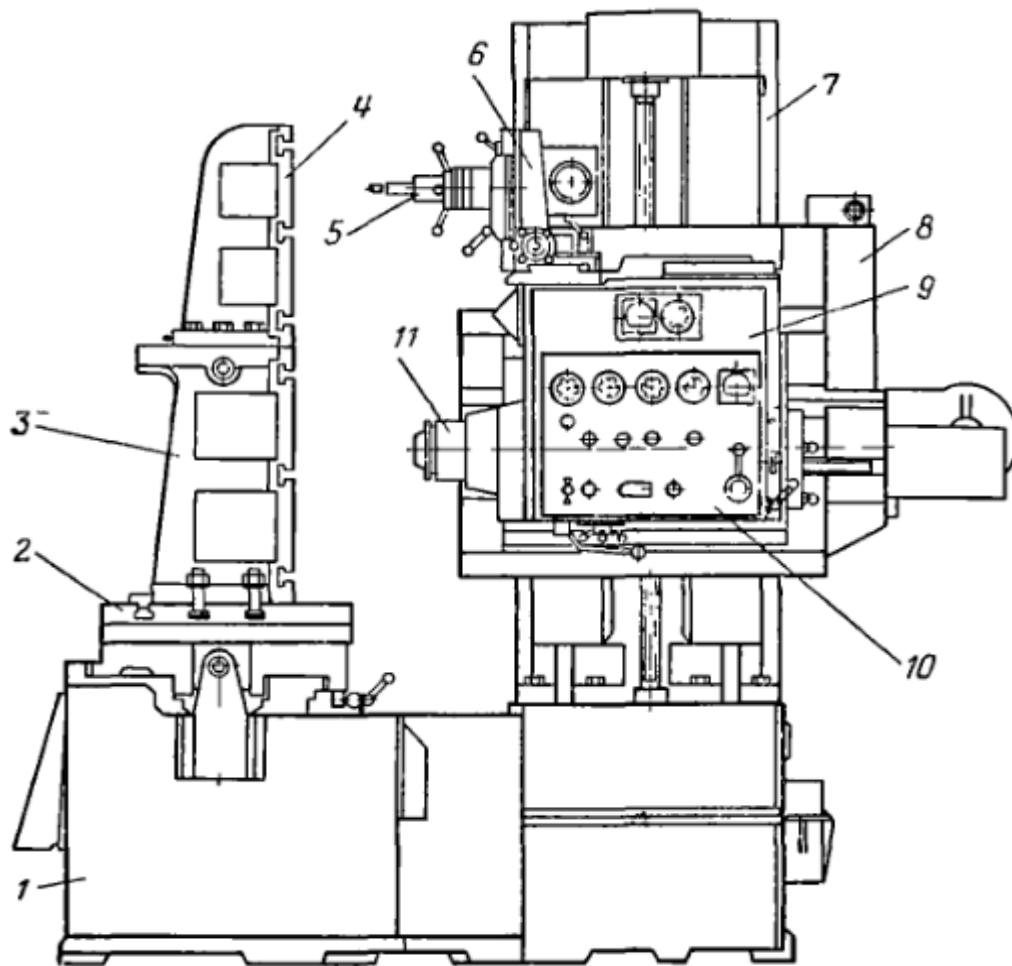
Копіювально-фрезерний верстат моделі 6441Б.
